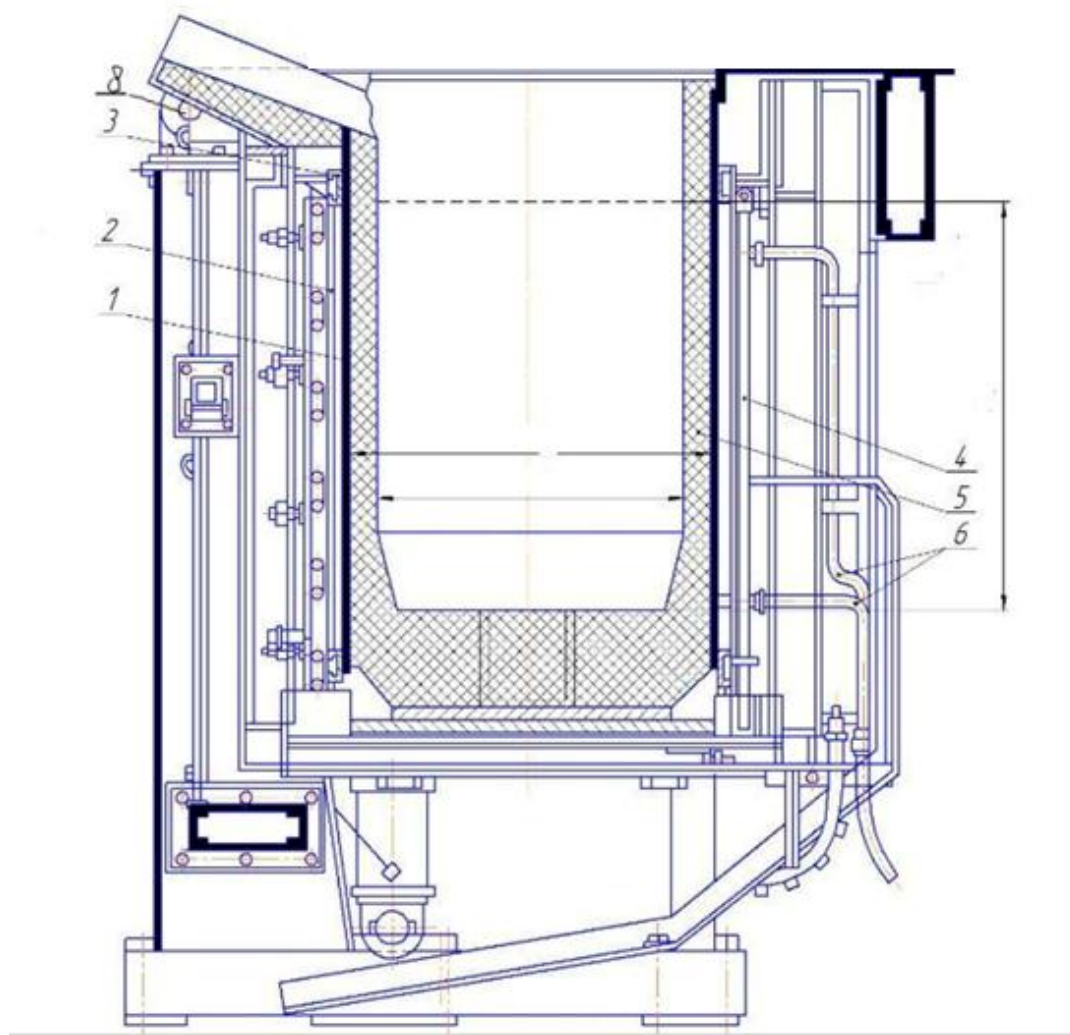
Схема індукційної сталеливарної печі – ІСТ 0,4:
